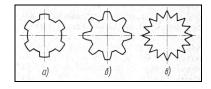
Виды шлицевых соединений: а – прямобочными шлицами ГОСТ 1139—80; б – эвольвентными шлицами; в – треугольными шлицами
